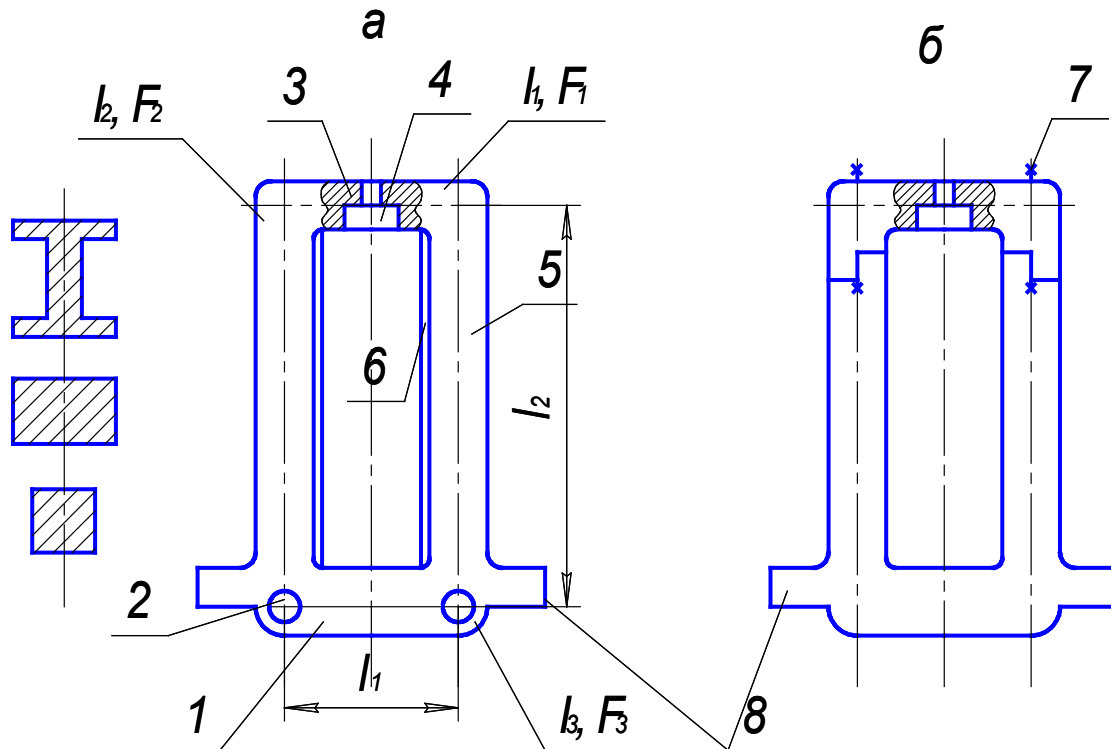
Станина робочої кліті: 1 - нижня поперечка; 2 - отвір для установки станинних роликів; 3 - верхня поперечка; 4 - отвір для натискної гайки; 5 - стійка; 6 - захисна планка; 7 - шпилька; 8 - лапа
